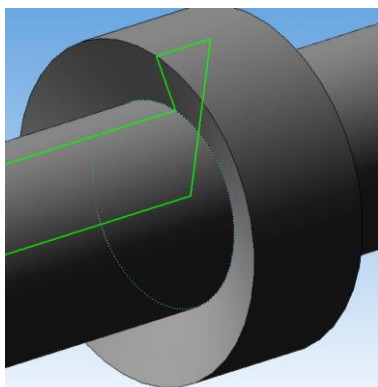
Излучатель состоящий из цилиндров различного диаметра
